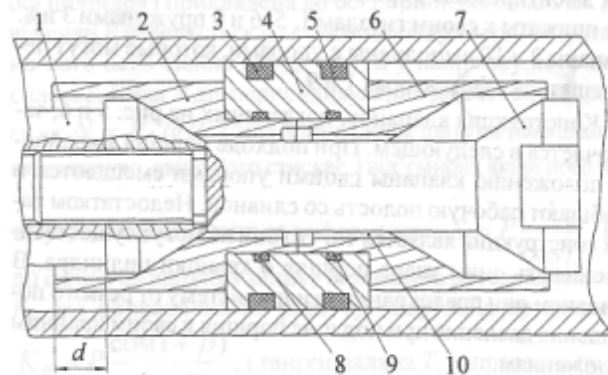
Конструкция плавающего поршня (перепускное устройство) ХАДИ (ХНАДУ).
